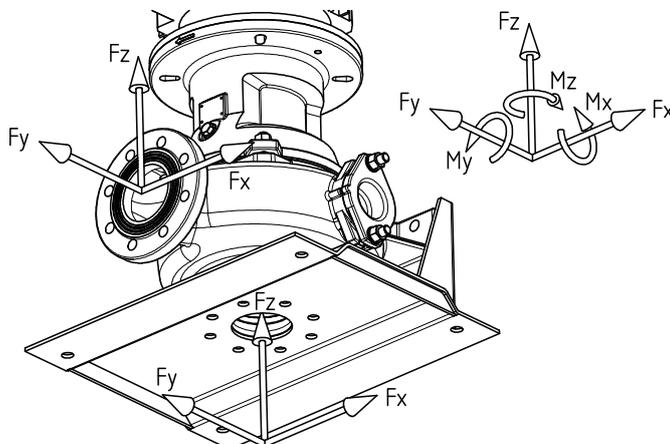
Fuerzas y pares en las bocas de la bomba, montaje vertical, con plancha de montaje
